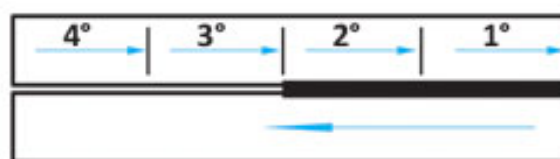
Técnica de soldagem passe 'a ré'. (ESAB, 2020)
